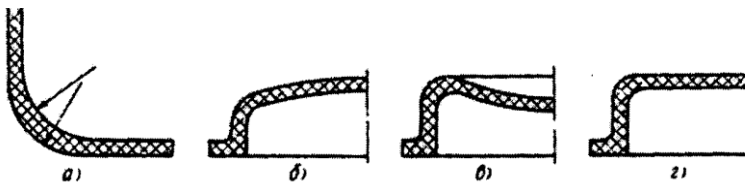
Варіанти конструкцій деталей з пластмас
